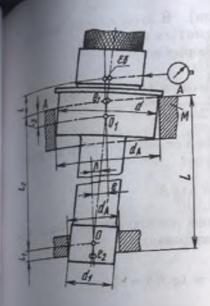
Схема установки детали на цилиндрической оправке по двум отверстиям
